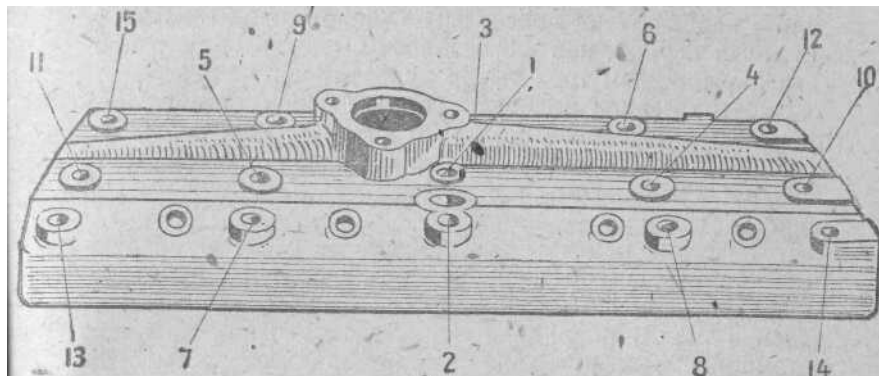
Последовательность, подтяжки болтов и гаек крепления головки блока цилиндров.
